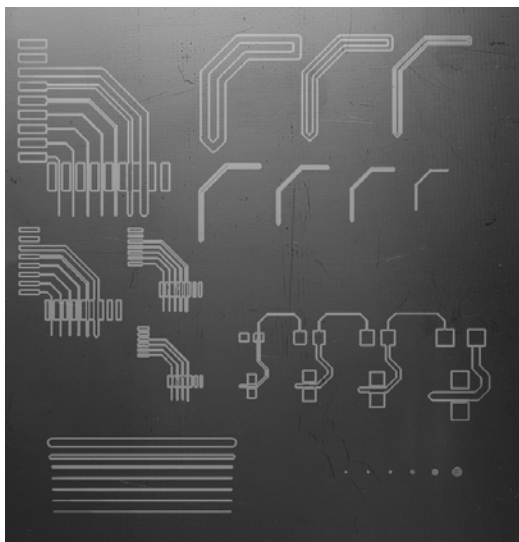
Печатная плата, полученная методом механической обработки фрезером
